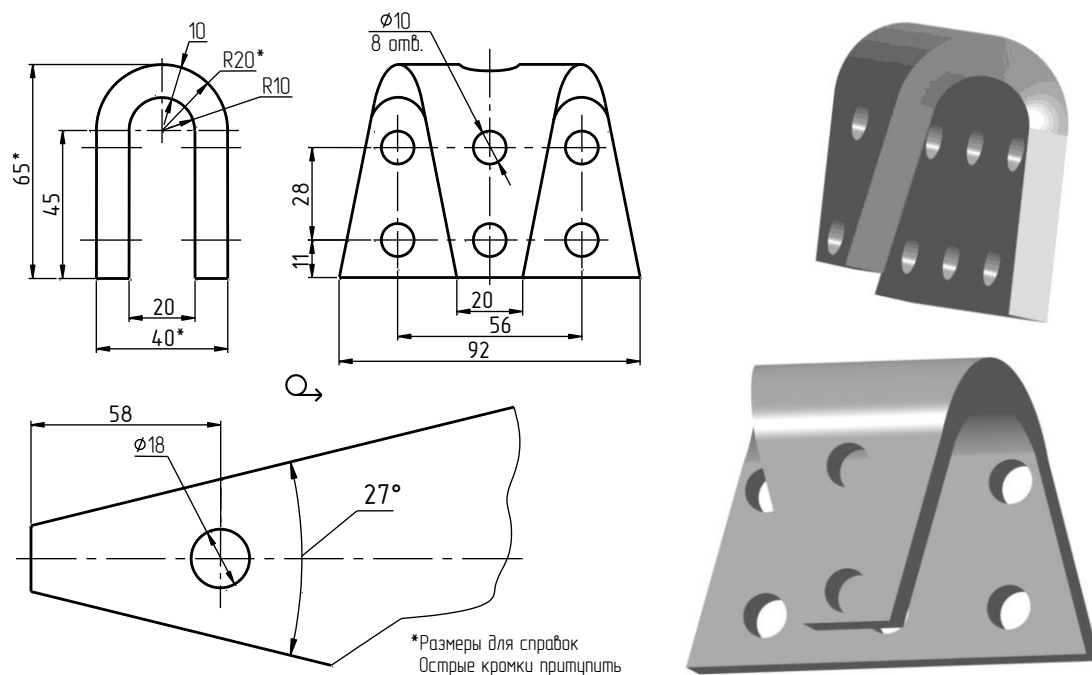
Чертеж детали, изготавливаемой *гибкой*, дополняют, при необходимости, разверткой ее заготовки для указания на ней тех размеров, которые невозможно указать на чертеже готовой детали
